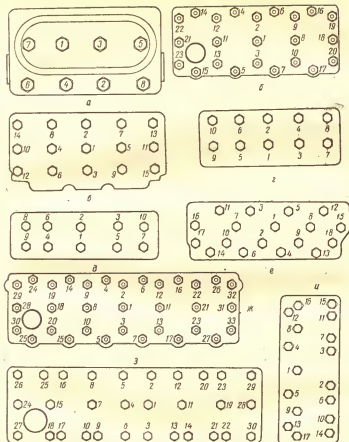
Последовательность затяжки гаек крепления головки блока цилиндров двигателей автомобилей:
